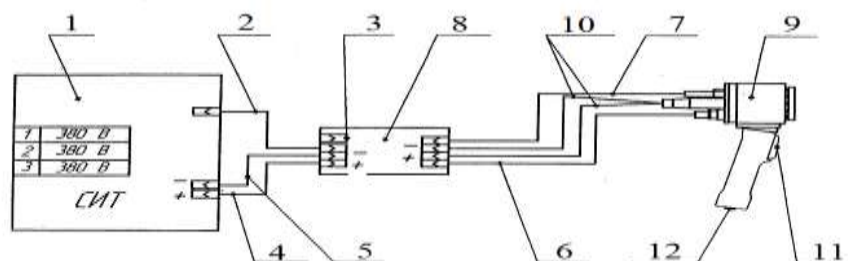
Схема металлизатора УЭМ-500 ТЛ : 1 - сварочный источник тока ВДУ-506С; 2 - кабель управления; 3 - ниппель подключения сжатого воздуха; 4 - кабель сварочный силовой «+»; 5 - кабель сварочный силовой «-»; 6 - кабель управления; 7 - шланг подачи сжатого воздуха на распыление; 8 - блок управления с подающим и размоточным устройствами; 9 - ручной электродуговой пистолет; 10 - кабель сварочный силовой; 11 - клавиша включения подачи проволоки (верхняя); 12 — кнопка подачи сжатого воздуха на распыление материала (блокировка включения ВДУ).
